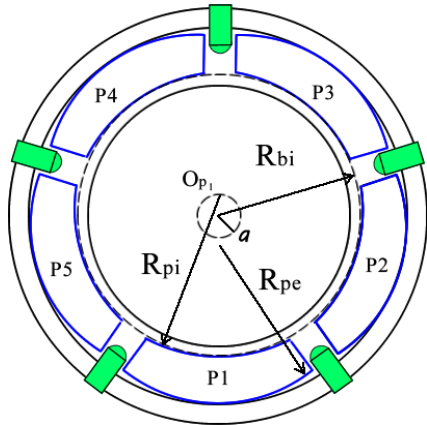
Schema del cuscinetto a cinque pattini oscillanti.
